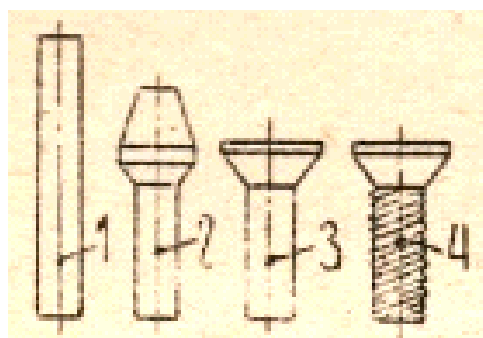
Переходы штамповки винта на холодновысадочном автомате: 1 — заготовка; 2 — предварительная высадка; 3 — высадка головки; 4 — накатка резьбы
